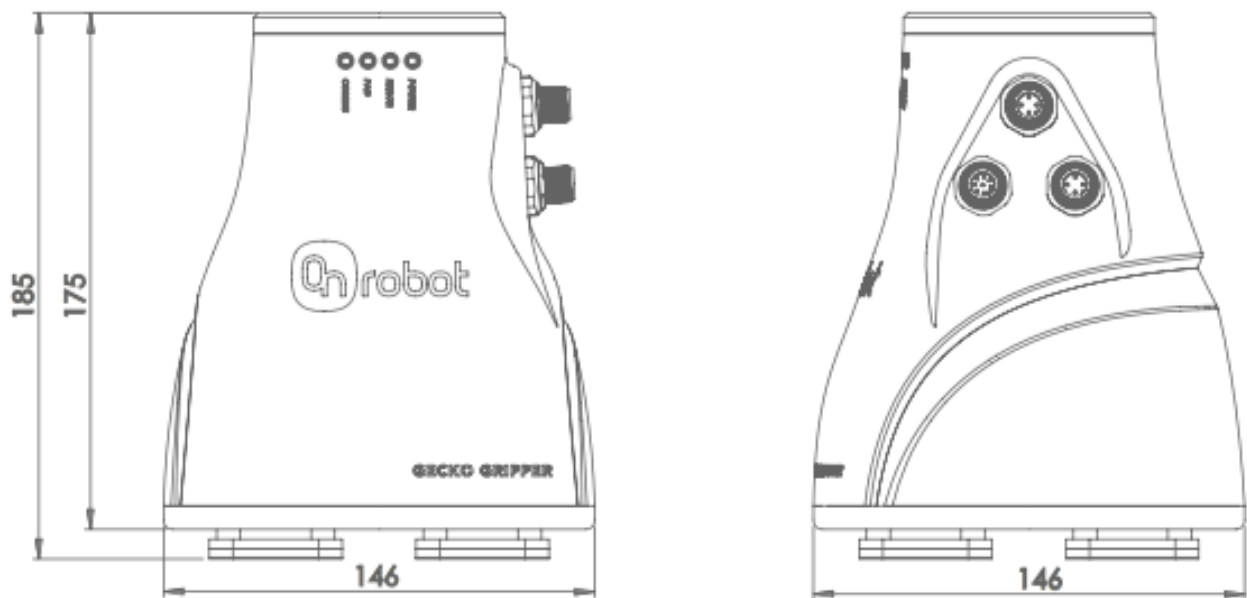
Dimensiones frontales y laterales de Gecko Gripper.
